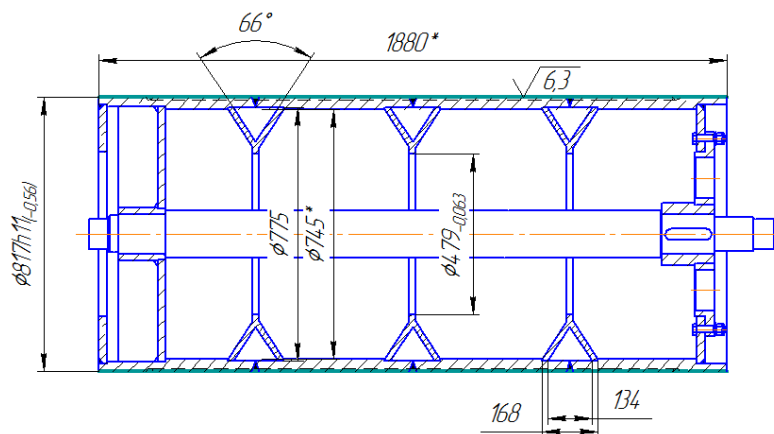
Барабан в сборе с треугольными усиливающими элементами
